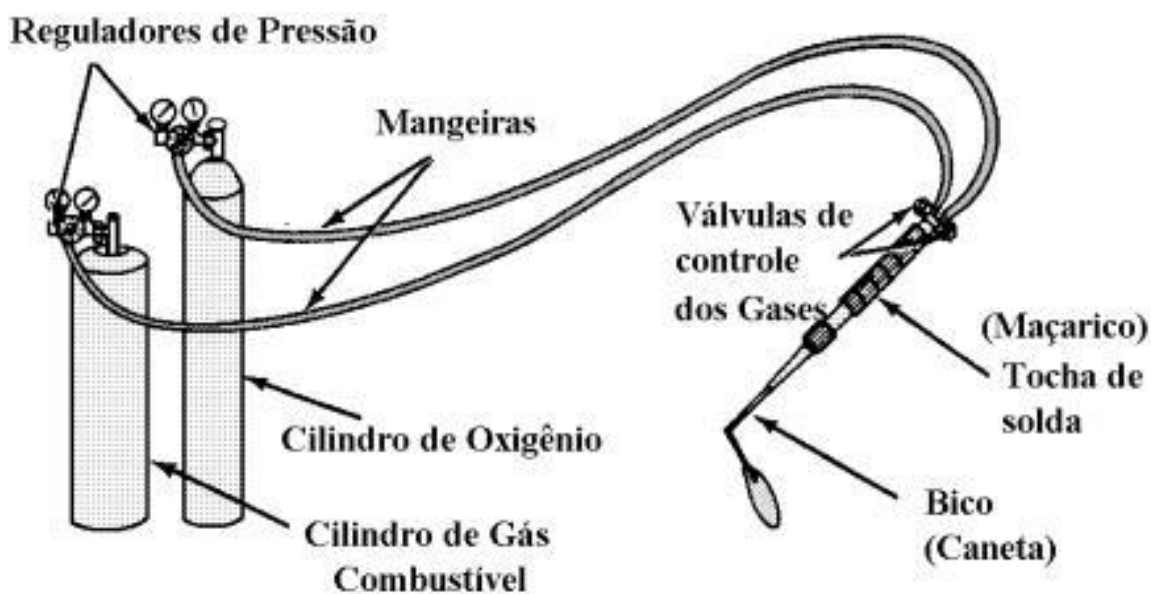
Esquema de funcionamento de garrafas de soldadura
